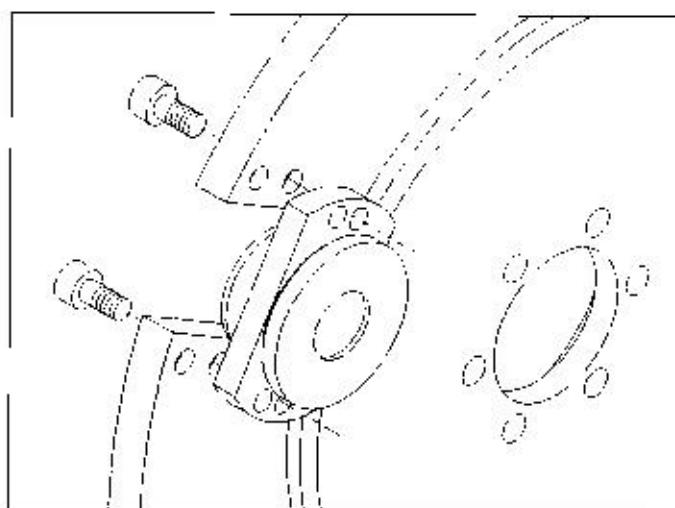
Сборка фланцевого планетарного держателя-фланцевого планетарного диска
